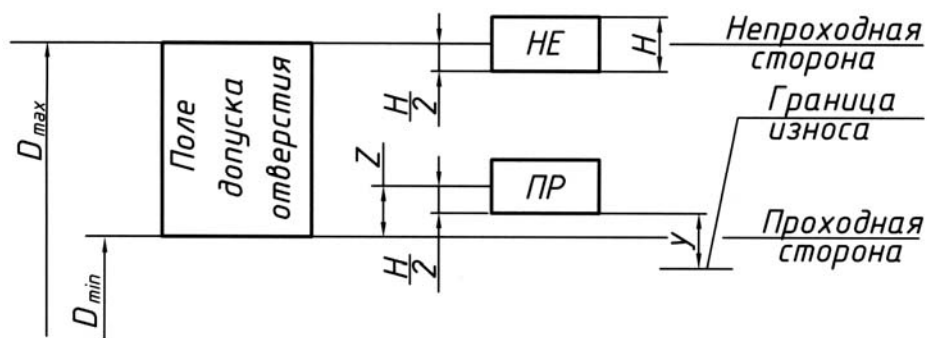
Схема расположения полей допусков калибров-пробок для размеров до 180 мм
